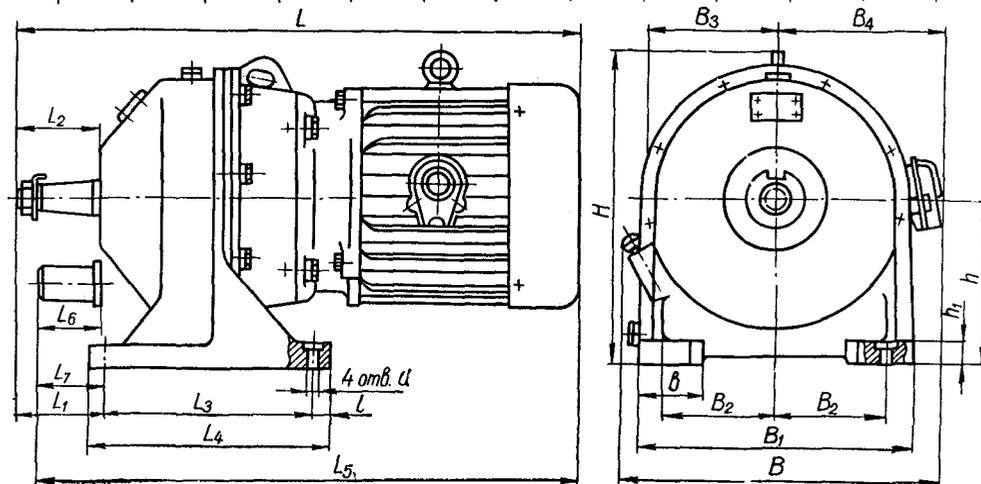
Основные и габаритные размеры мотор-редуктора МРА.
